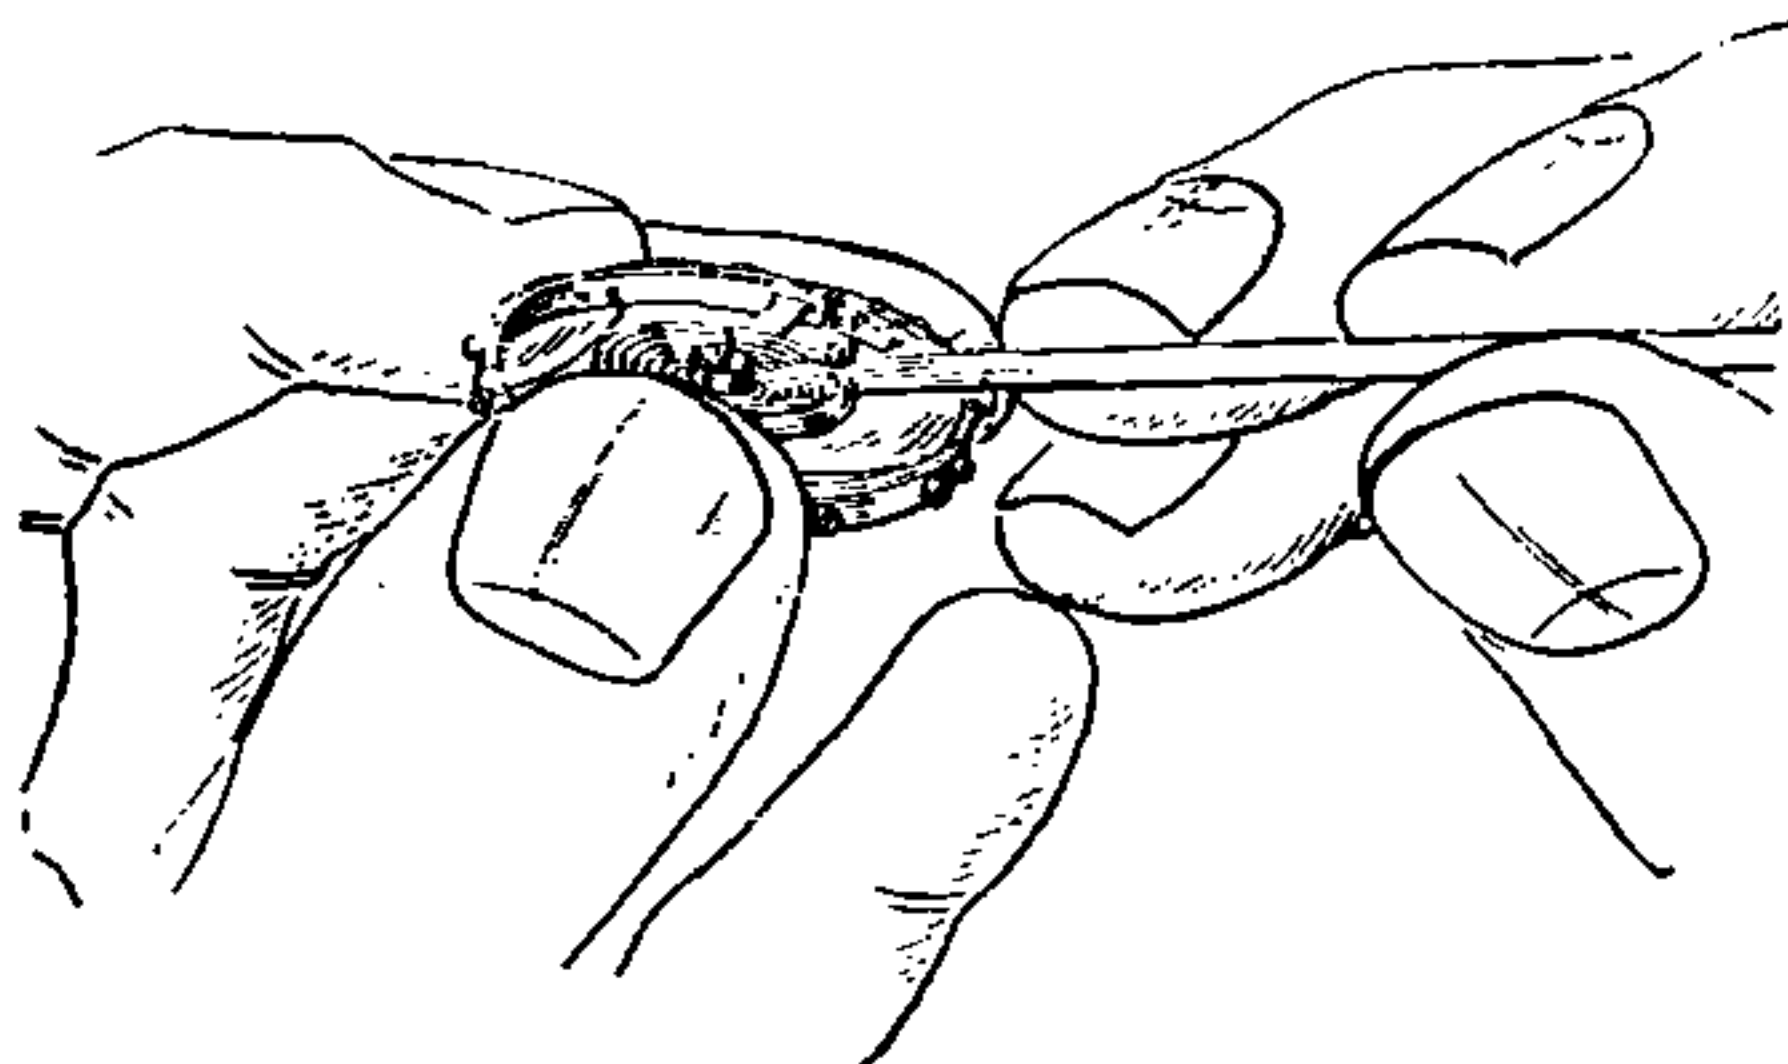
Smontaggio della spirale mediante spinta da sotto.
